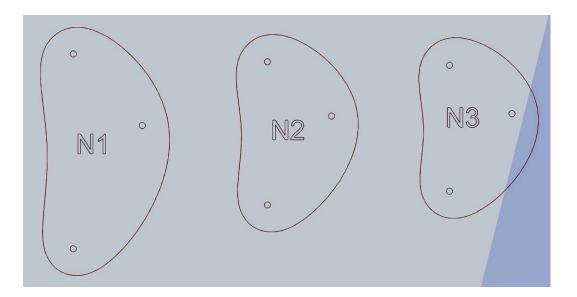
Plantillas para empalme cilíndrico. Elaboración propia, septiembre 2018.
